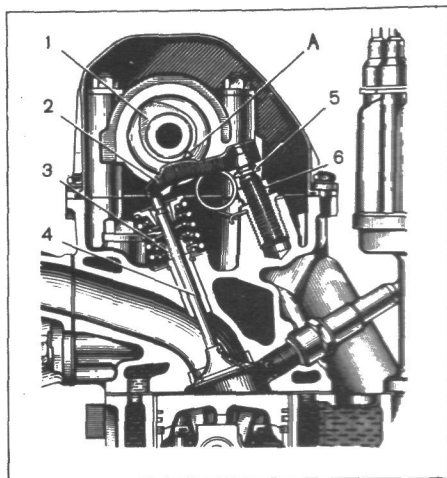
Механизм газораспределения: 1 — кулачок распределительного вала; 2 — рычаг привода клапана; 3 — маслоотражательный колпачок клапана; 4 — клапан; 5 — регулировочный болт рычага; 6 — контргайка регулировочного болта
